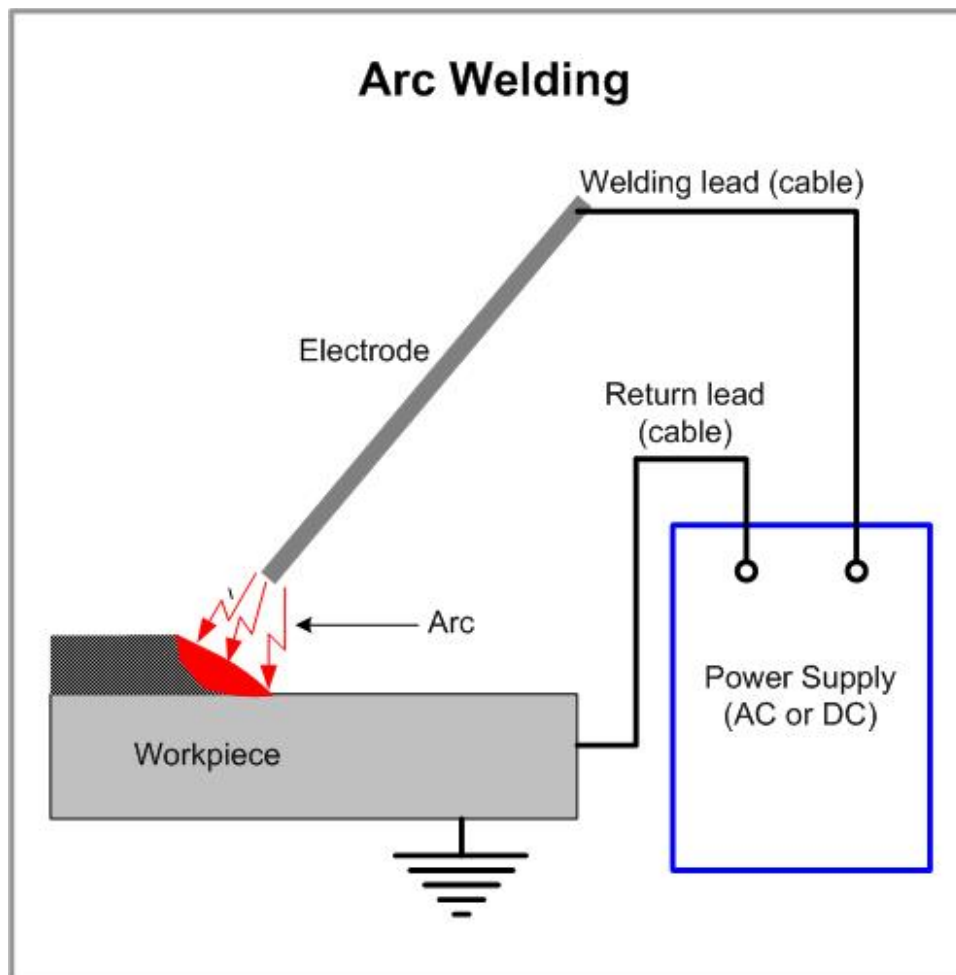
Dibujo donde se representan las partes más importantes de la soldadura por arco, y el arco que se produce entre el electrodo y la pieza.
